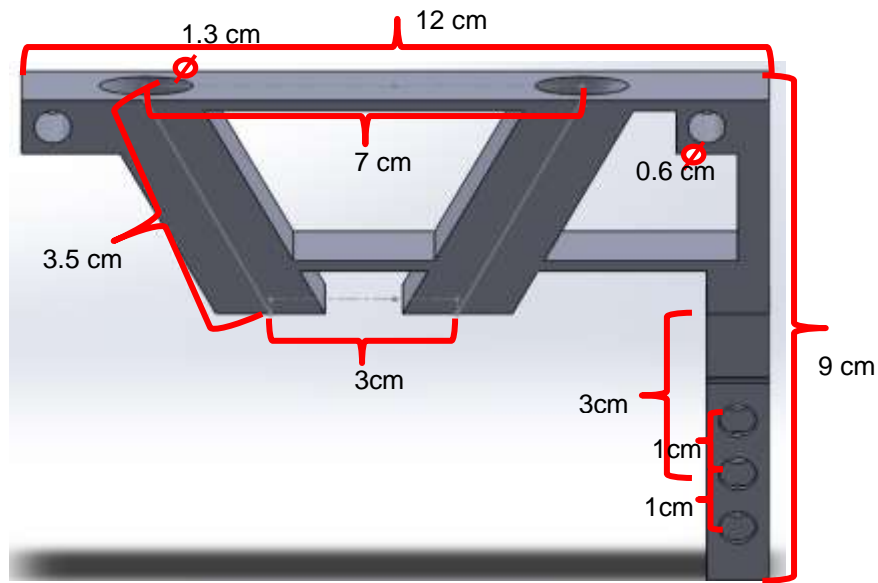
Diseño en Solidworks de la parte superior del prototipo.
